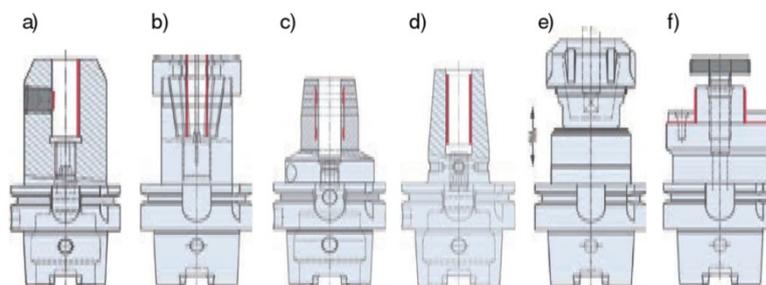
Werkzeughalter: a) Flächenspann-, b) Spannzangen-, c) Hydrodehnspann-, d) Schrumf-, e) Gewindeschneidfutter, f) Aufsteckfräserdorn; Quelle: Taschenbuch der Werkzeugmaschinen, Hanser
